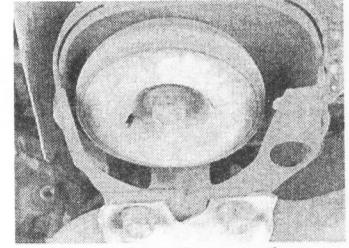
д. Задний болт крепления подрамника к корпусу автомобиля.
